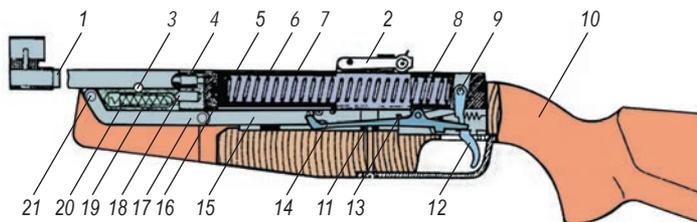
Устройство пневматической винтовки ИЖ-38: 1 — ствол; 2 — прицел; 3 — ось ствола; 4 — прокладка ствола; 5 — коробка ствольная; 6 — поршень; 7 — пружина боевая; 8 — колодка механизма спускового; 9 — штифт колодки; 10 — ложа; 11 — винт ложи задний; 12 — крючок спусковой; 13 — шептало; 14 — рычаг блокировки; 15 — рычаг взведения; 16 — манжета; 17 — шарнир; 18 — клин; 19 — ригель; 20 — пружина ригеля; 21 — ось шарнира
